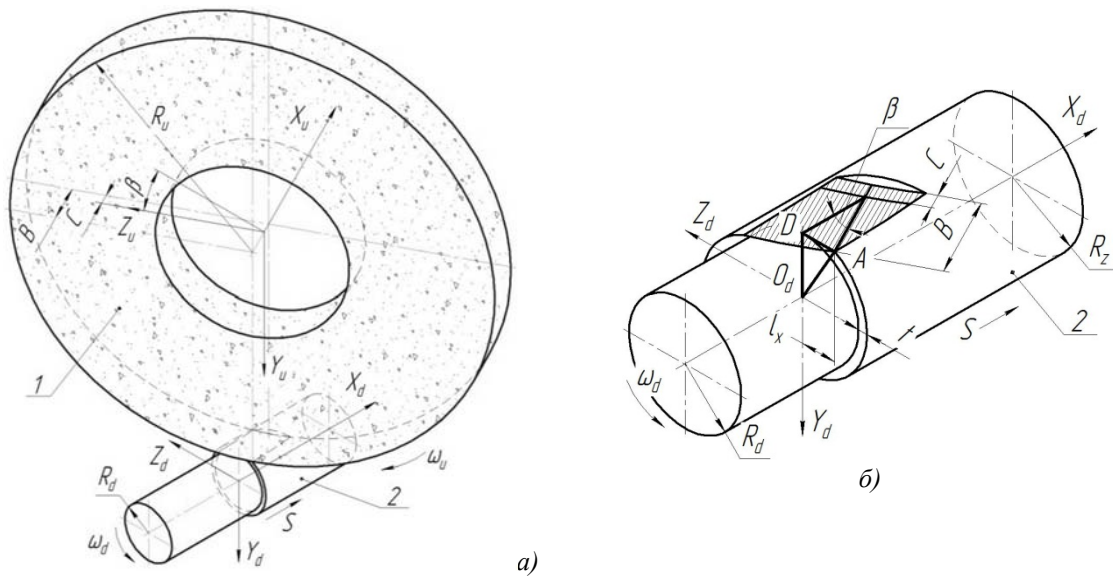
Схема однопрохідного доводочного шліфування зі схрещеними осями інструмента та деталі
